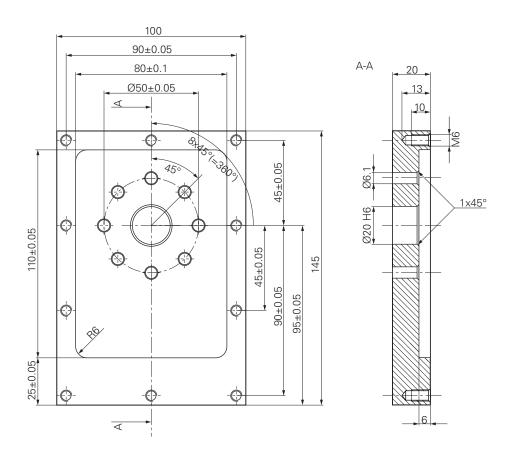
Beispielwerkstück – Technische Zeichnung
